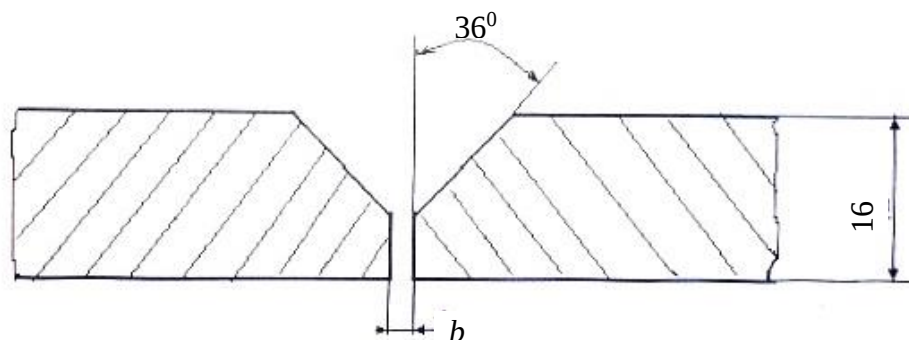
Конструктивнi елементи пiдготовлення кромки
